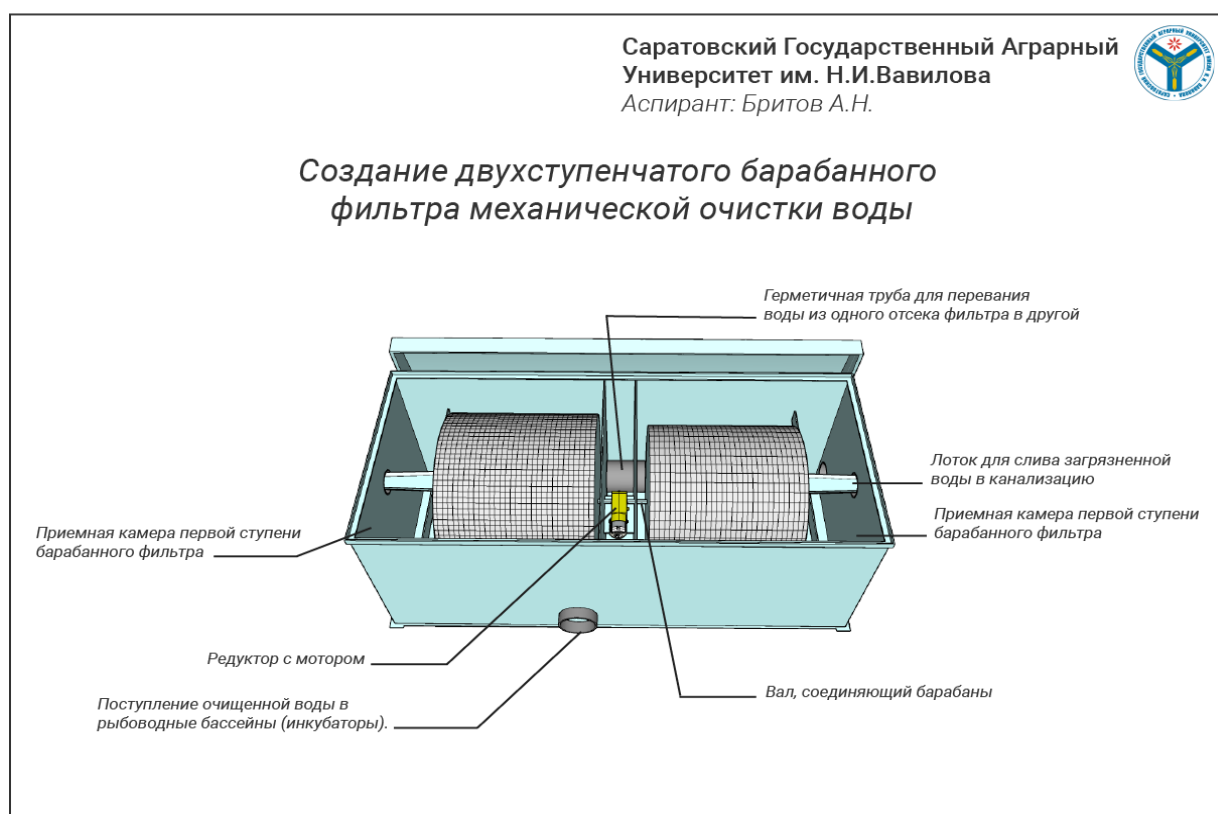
Двухступенчатый барабанный фильтр механической очистки воды
